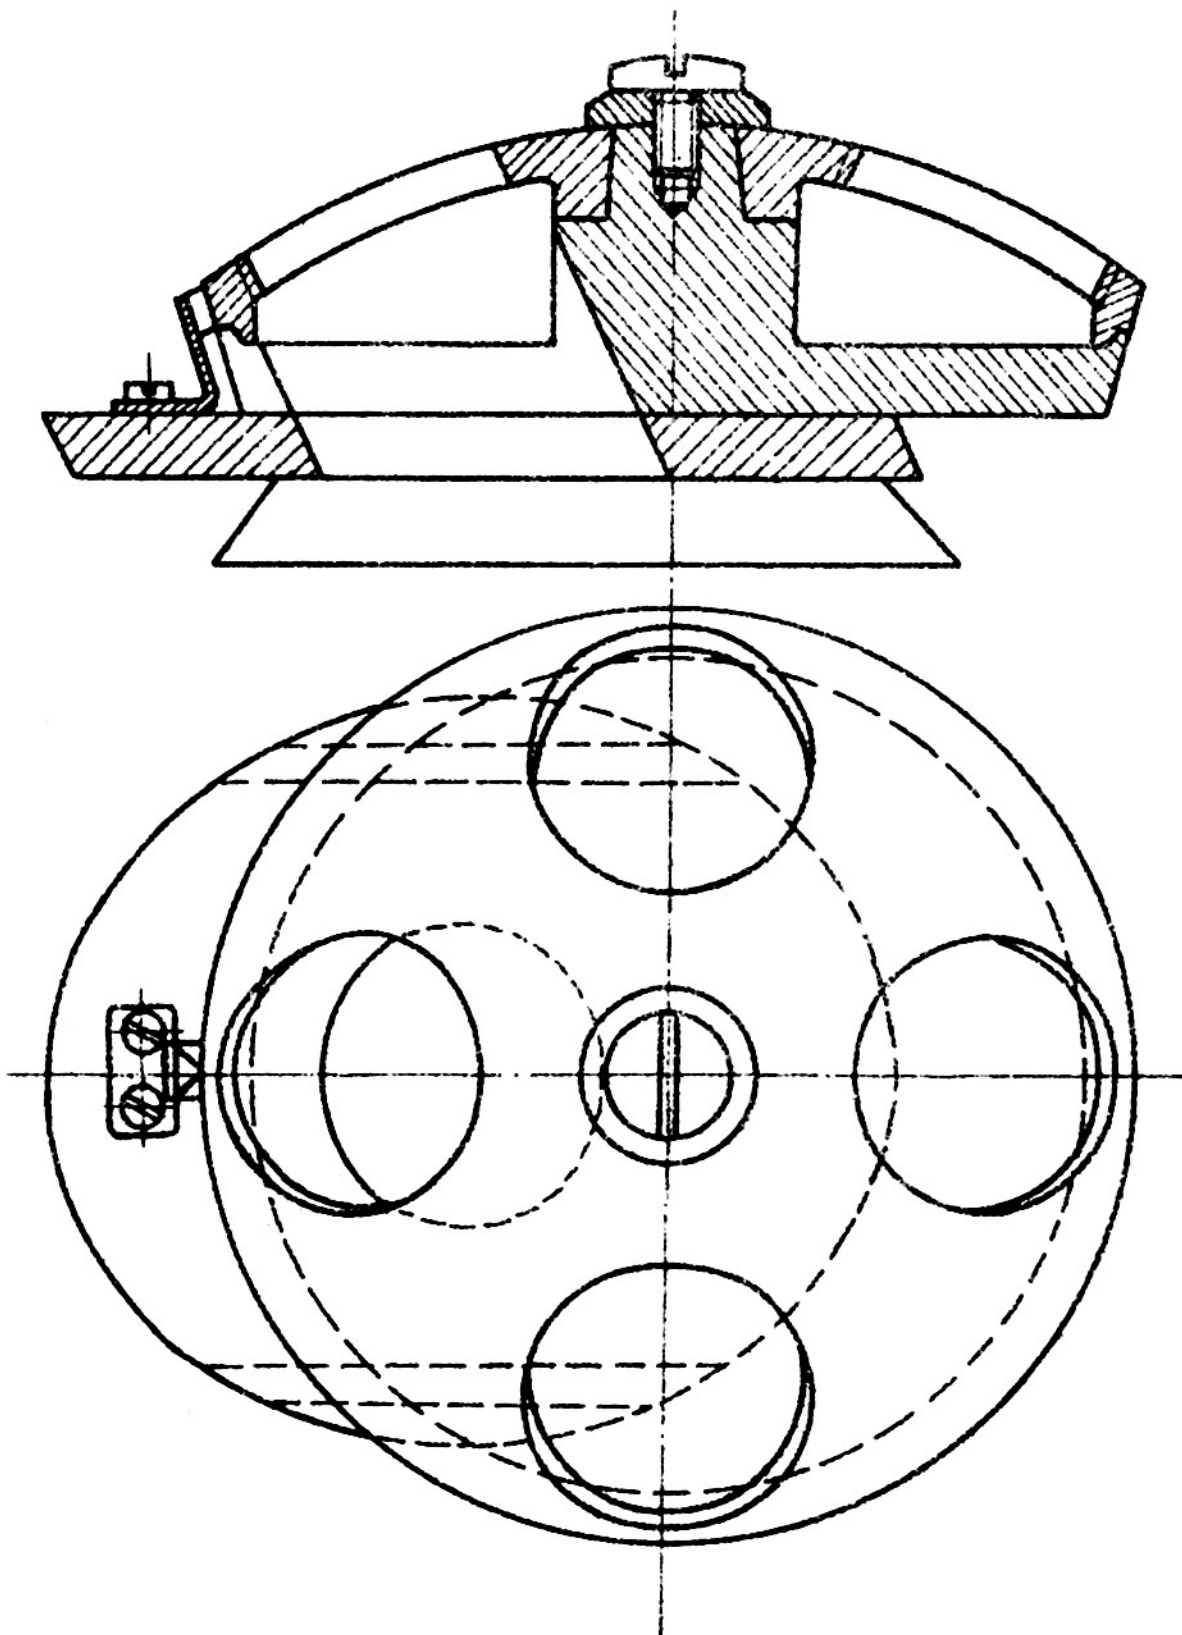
Detailní konstrukce zařízení pro hrubý a jemný posuv mikroskopu
